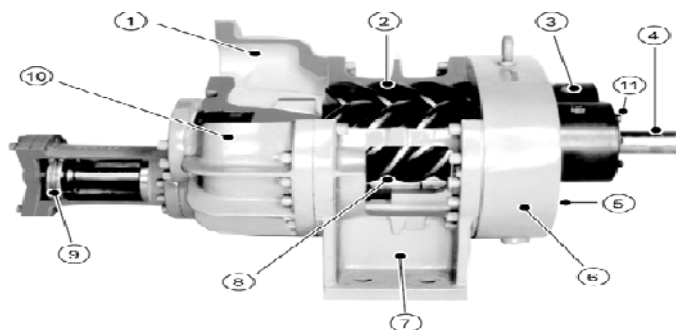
Vue en coupe partielle d'un compresseur à vis birotor.
